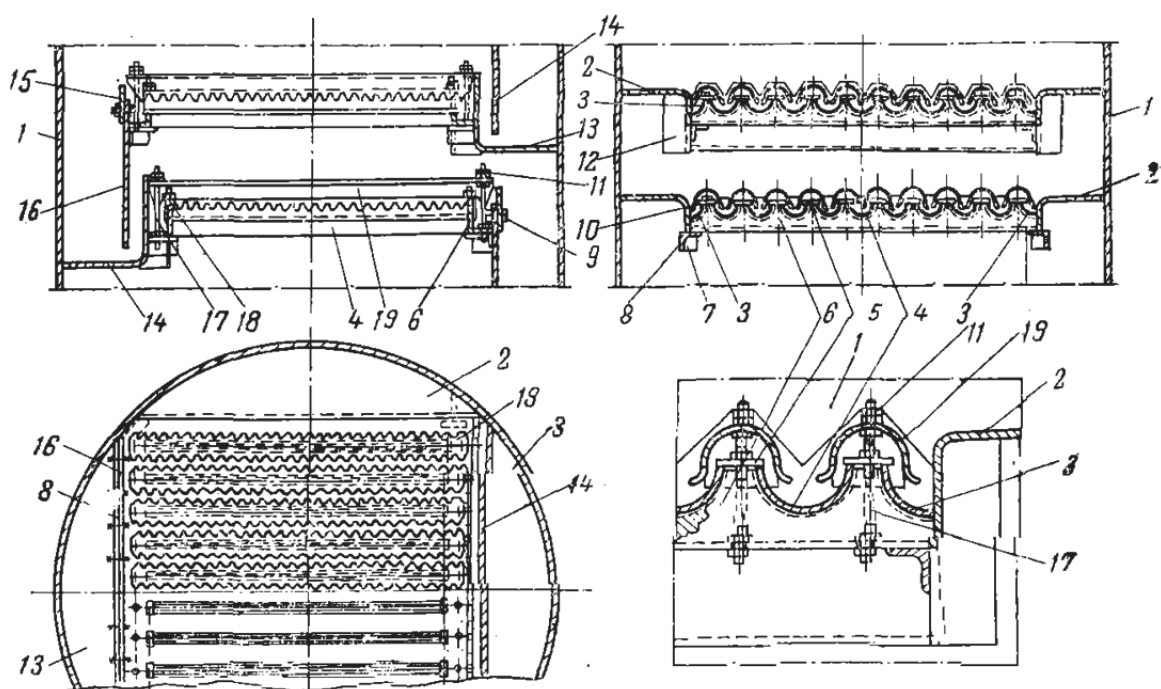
Конструкция тарелки с желобчатыми элементами: 1 – корпус колонны; 2 – глухие сегменты; 3 – полужелоба; 4 – желоб; 5 – прямоугольная шайба; 6 – опорный уголок; 7, 8, 12 – уголки; 9 – болт для крепления сливной планки; 10 – гайка для крепления желоба; 11 – гайка; 13 – карманы; 14 – сливная перегородка; 15 – сливная планка; 16 – сливная перегородка; 17 – шпилька для крепления колпачка; 18 – шпилька для крепления желоба; 19 – колпачок
